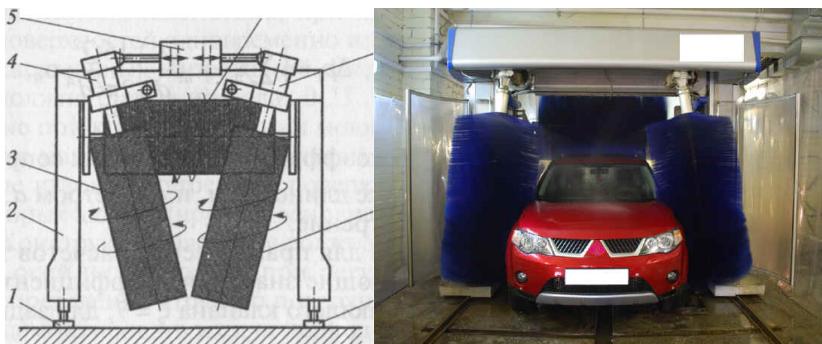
Устройство щеточной моечной установки портального типа:
